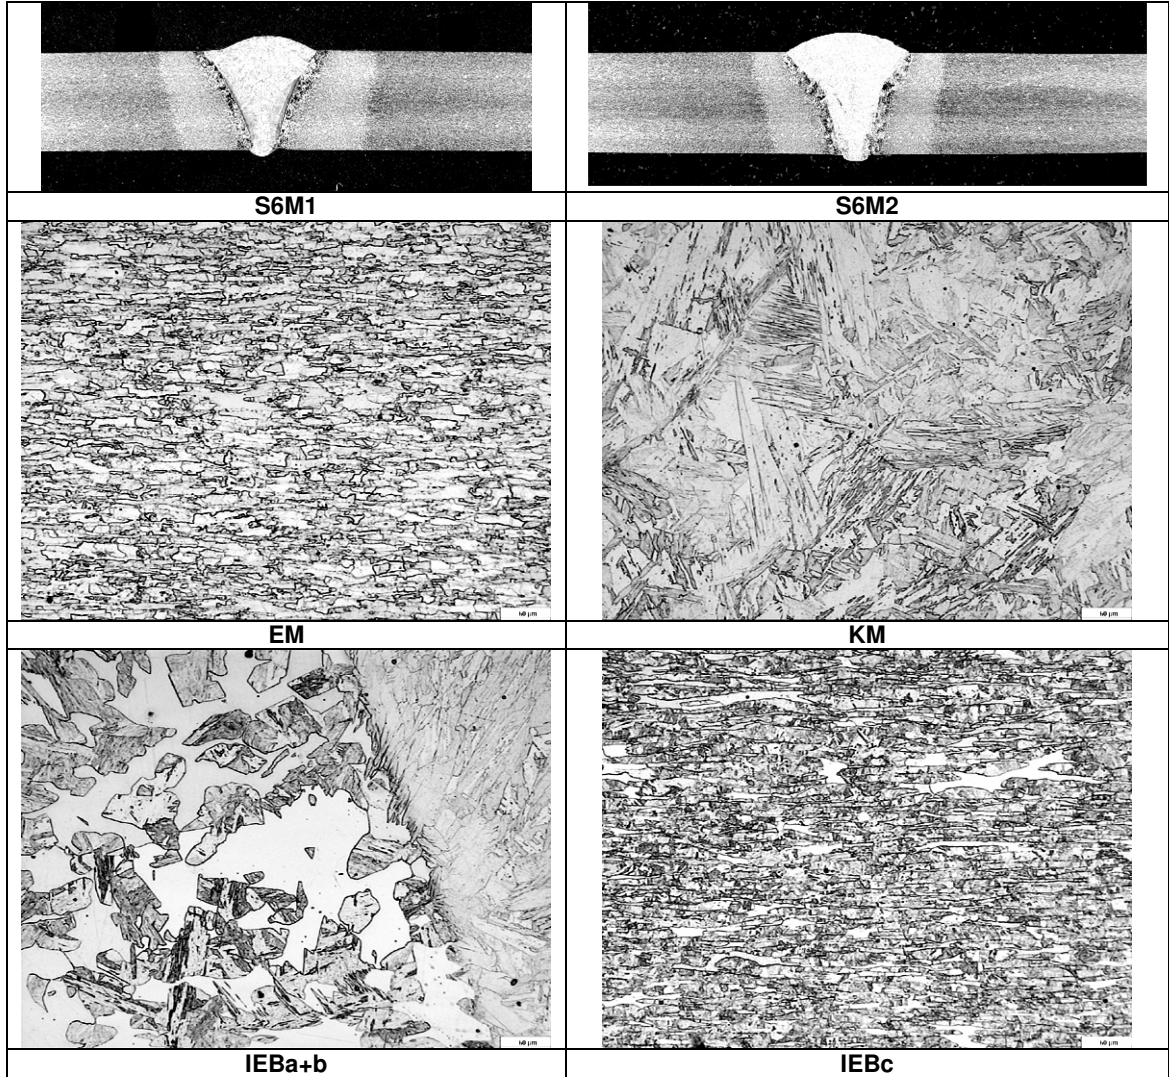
6 mm kalınlığında GMAW kaynaklı bağlantının makro ve mikroyapıları (R9).
